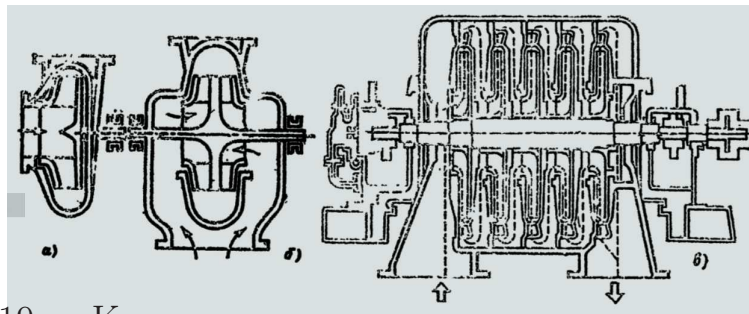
Конструктивные схемы лопастных центробежных компрессоров: а - одностороннего входа; б - двухстороннего входа; в - многоступенчатый
